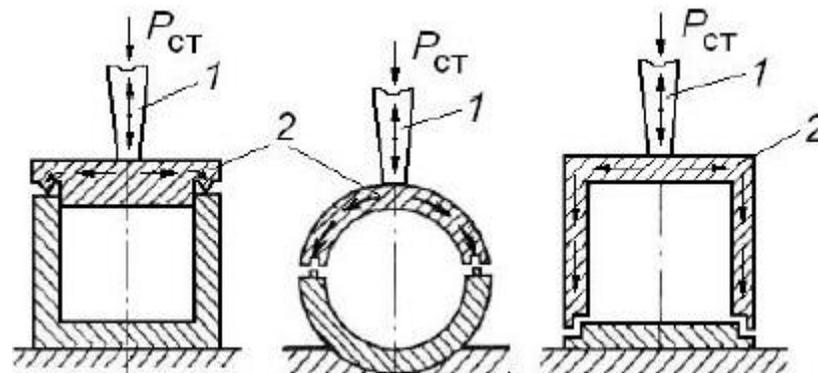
Схема передаточной ультразвуковой сварки: 1 – волновод; 2 – свариваемое изделие
